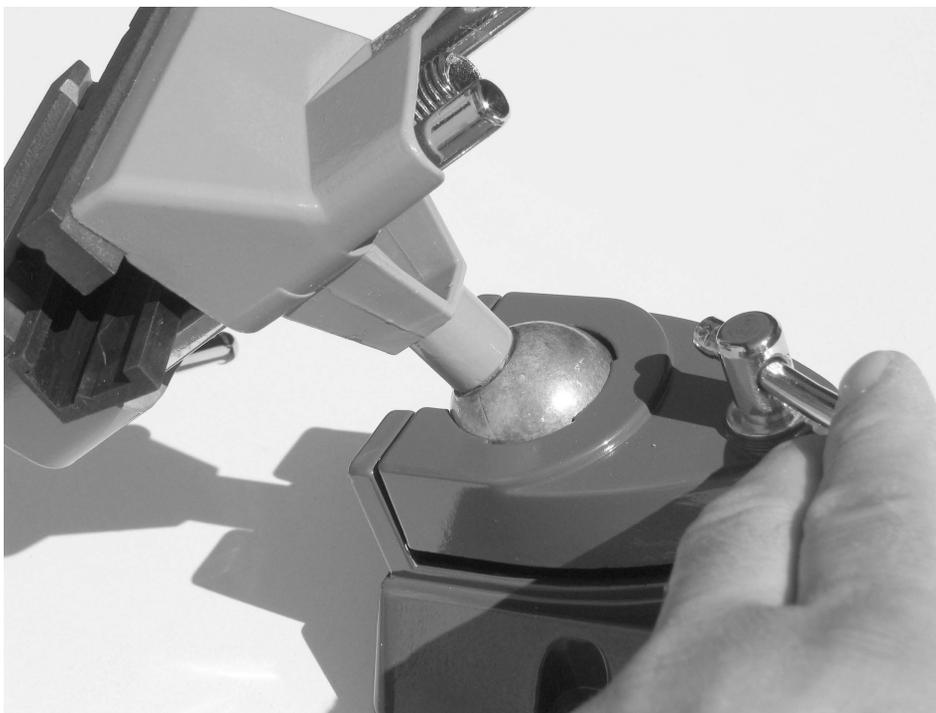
Mit der aufsteckbaren Spannzwinde lässt sich der Schraubstock an jeder Tischplatte befestigen.
